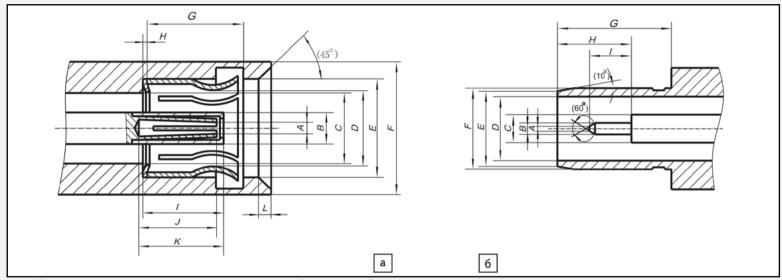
Интерфейс соединителя тип Mini-BMA: a) розетка; б) вилка
